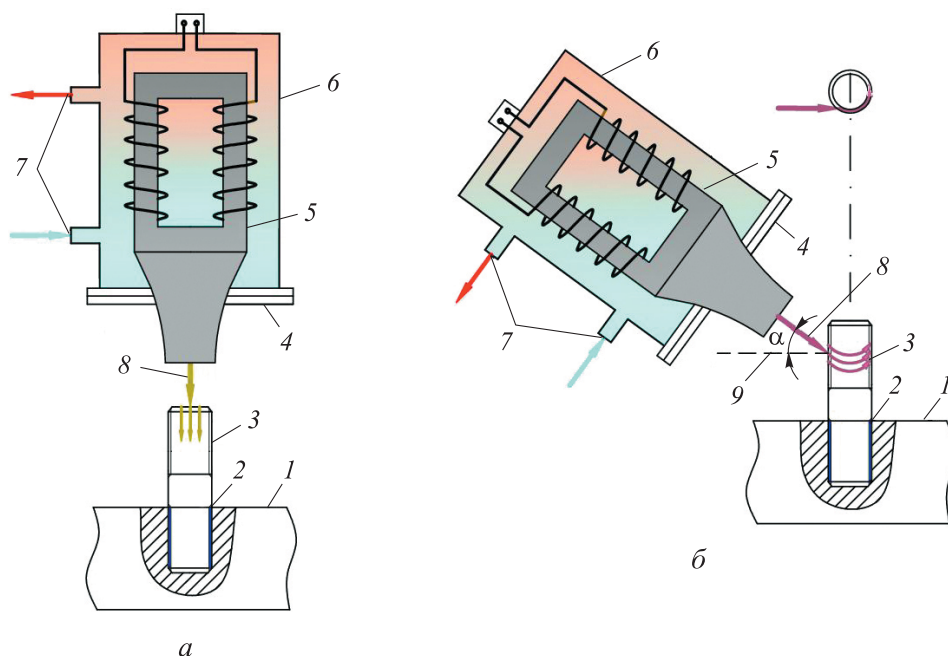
Схема ввода ультразвуковых волн с помощью магнитострикционного преобразователя в резьбовое соединение шпильки и соединяемой детали с торцевой поверхности (а) и под углом к боковой поверхности (б) шпильки:
